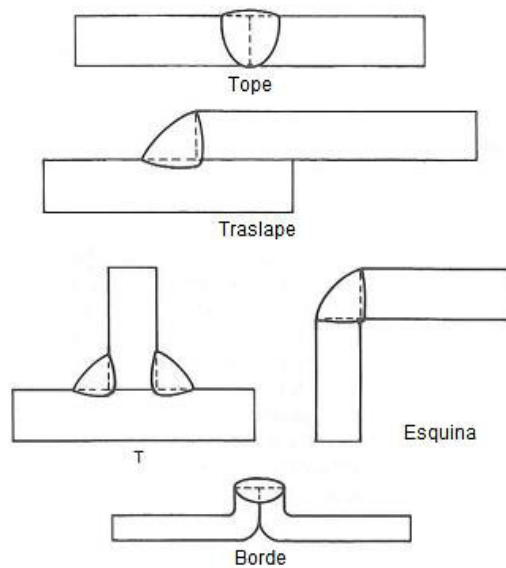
Juntas típicas de soldadura. [11]
